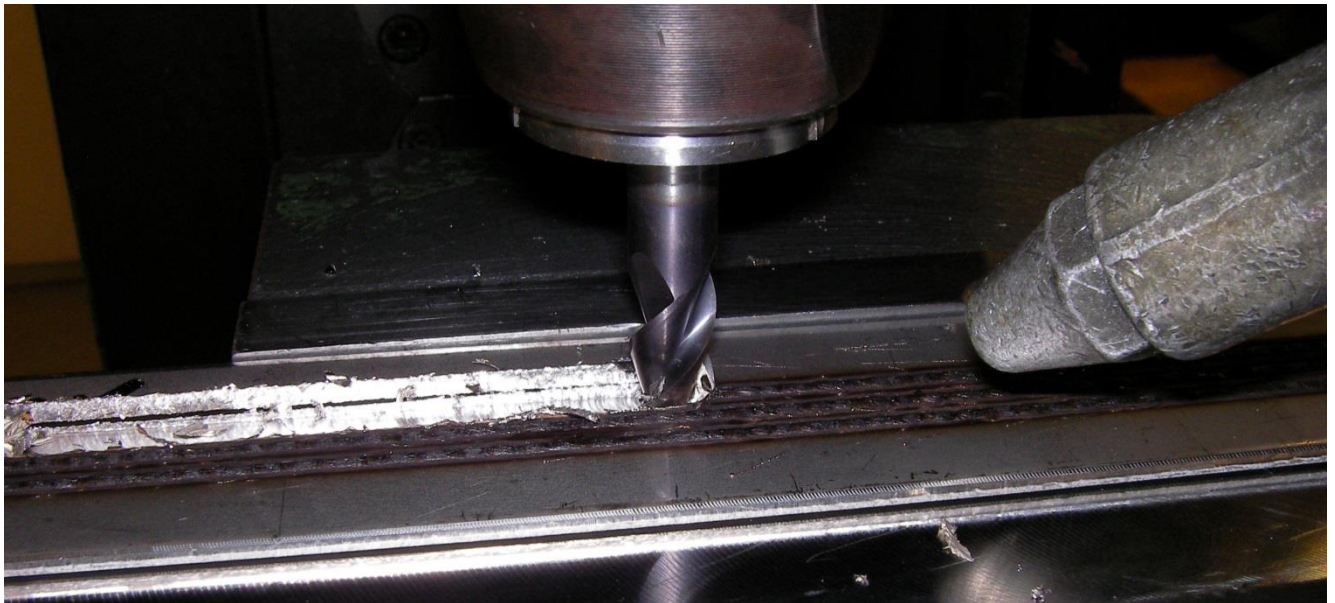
Abfräsen der Schweißnaht mittels Schaftfräser
